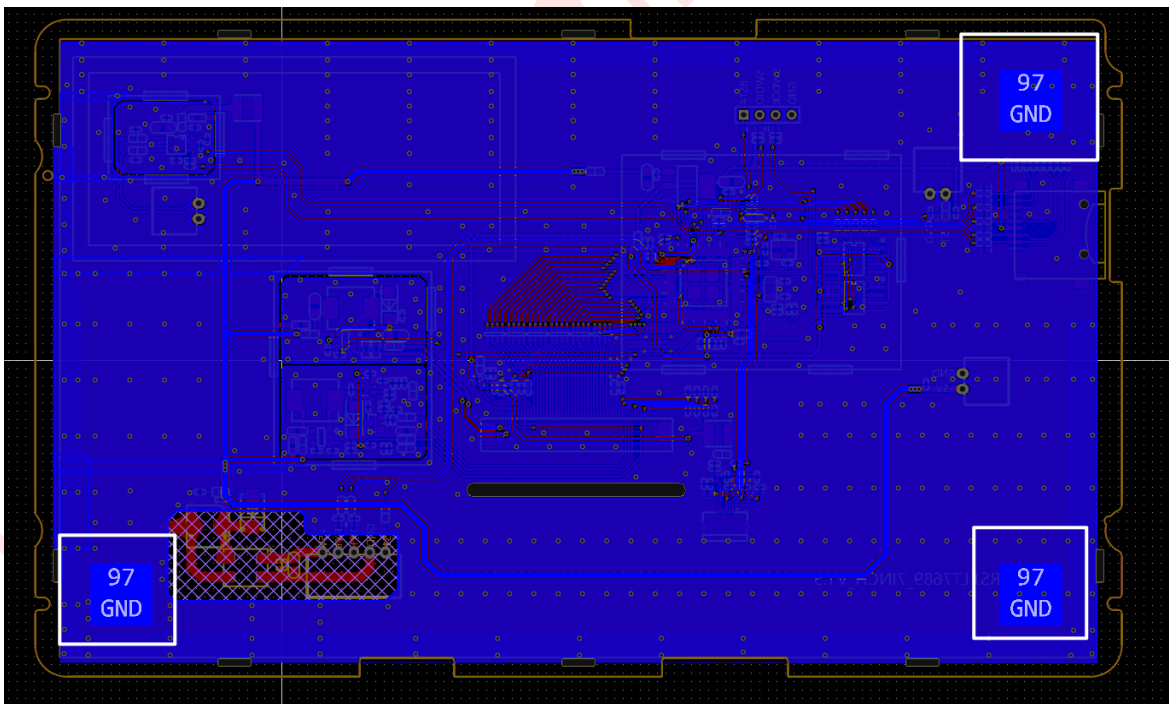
：PCB 上的 GND 焊盘示意图
